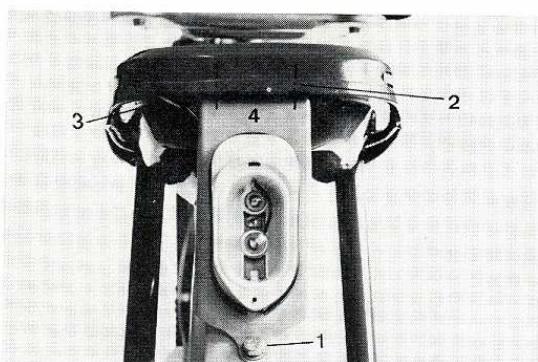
DÉMONTAGE DE LA PLAQUE DE FIXATION DU FEU ARRIÈRE.
